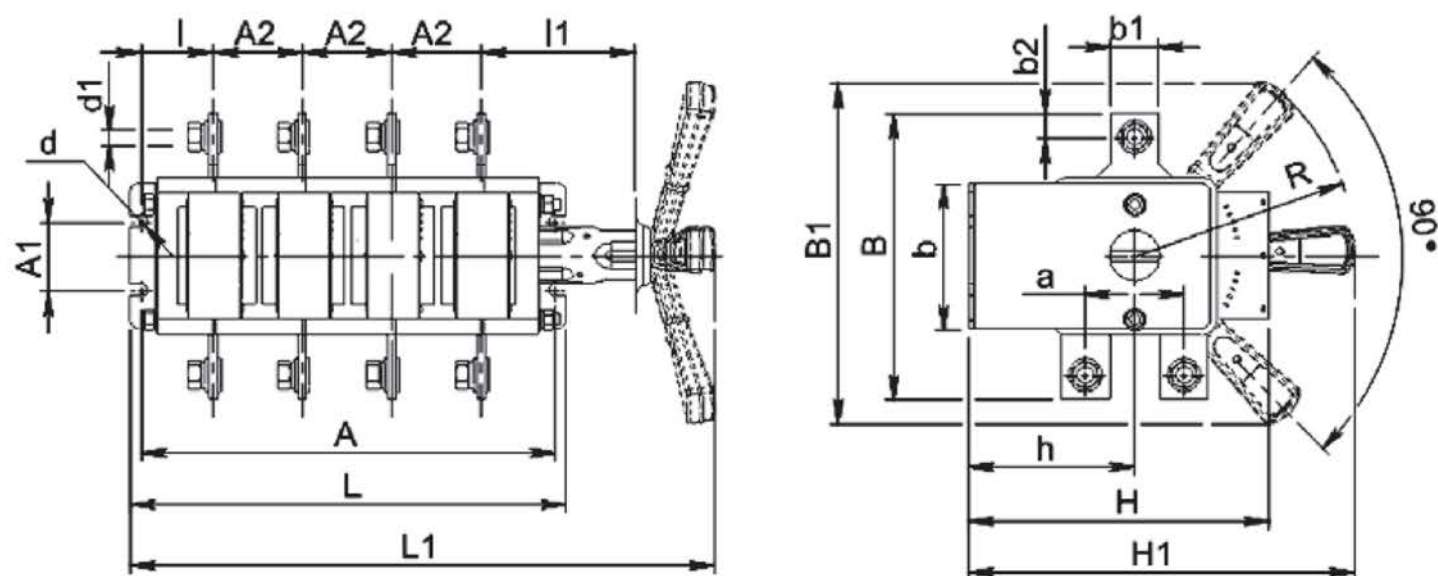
Выключатель-разъединитель четырехполюсный на два направление с боковой смещенной рукояткой.
